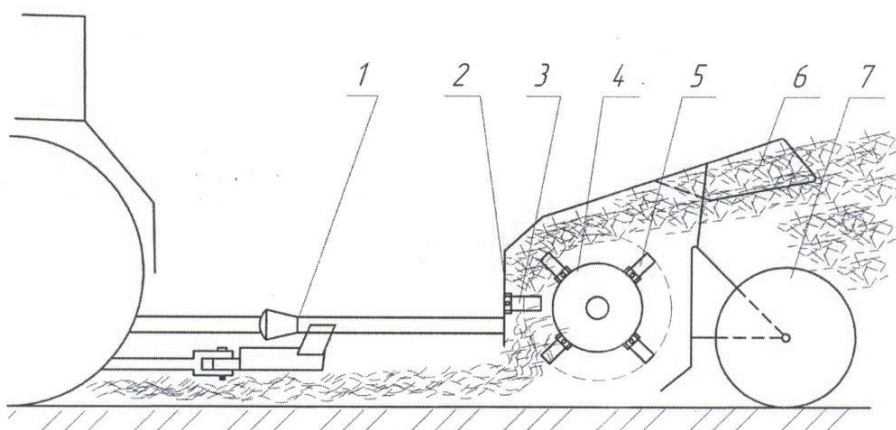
Технологическая схема 1 прицепного: 1 - карданный вал; 2 - корпус; 3 - противорезы; 4 - роторный подбирающий аппарат (измельчающий барабан); 5 - нож измельчающего барабана; 6 - разбрасыватель; 7 - колесо
